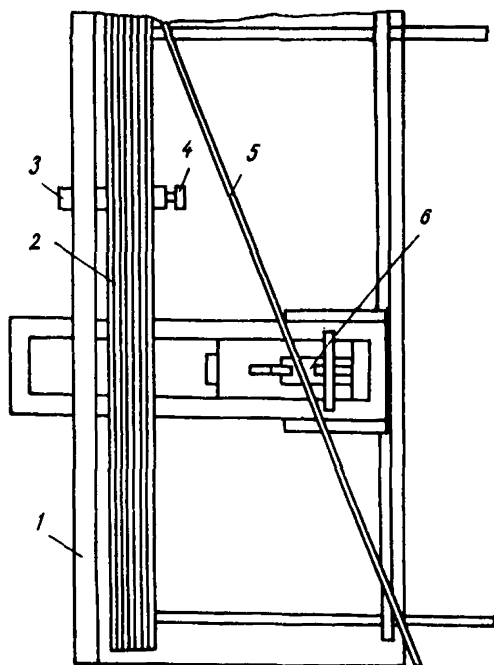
Отбор стержней из пакета с помощью подвижного механизма захвата и толкателей
